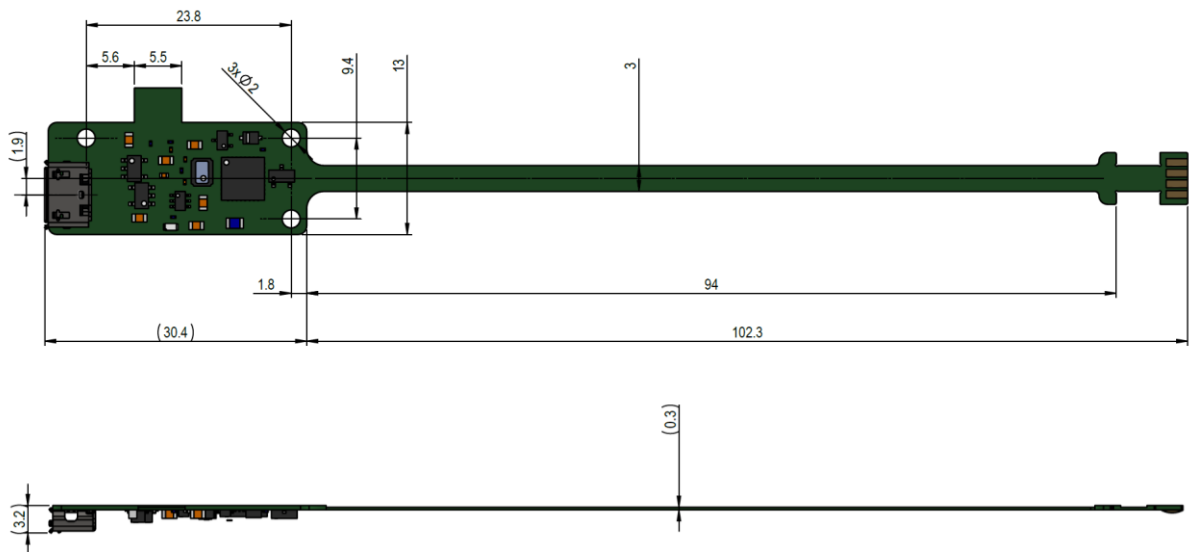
LSR-5 柔性电子组件机械示意图 (单位: mm)
